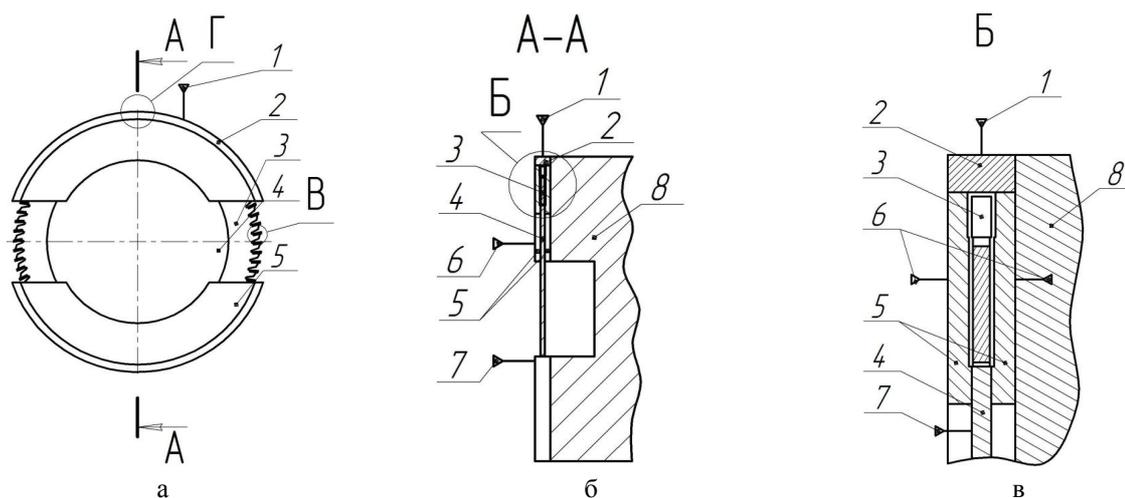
Принципиальная схема круглопильного станка с пневмоприводом кольцевой пилы: 1, 6, 7 – подводящий воздухопровод; 2 – воздухопровод с соплами; 3 – кольцевая пила; 4 – опорный диск; 5 – боковые направляющие пилы; 8 – станина
